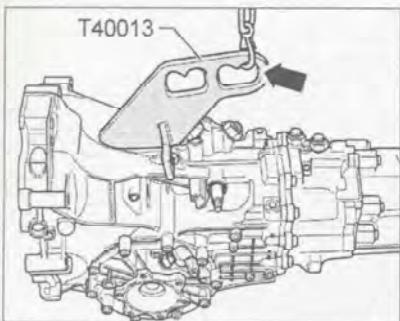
Закрепите приспособление для транспортировки T40013 в отверстии корпуса коробки передач. Сдвиньте механизм приспособления до упора. Подцепите краном устройство для транспортировки за четвертую проушину (стрелка).
